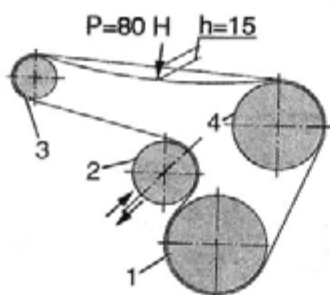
Схема натяжения ремня привода агрегатов:
